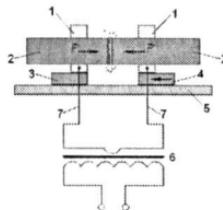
Схемастыковой электроконтактной сварки
